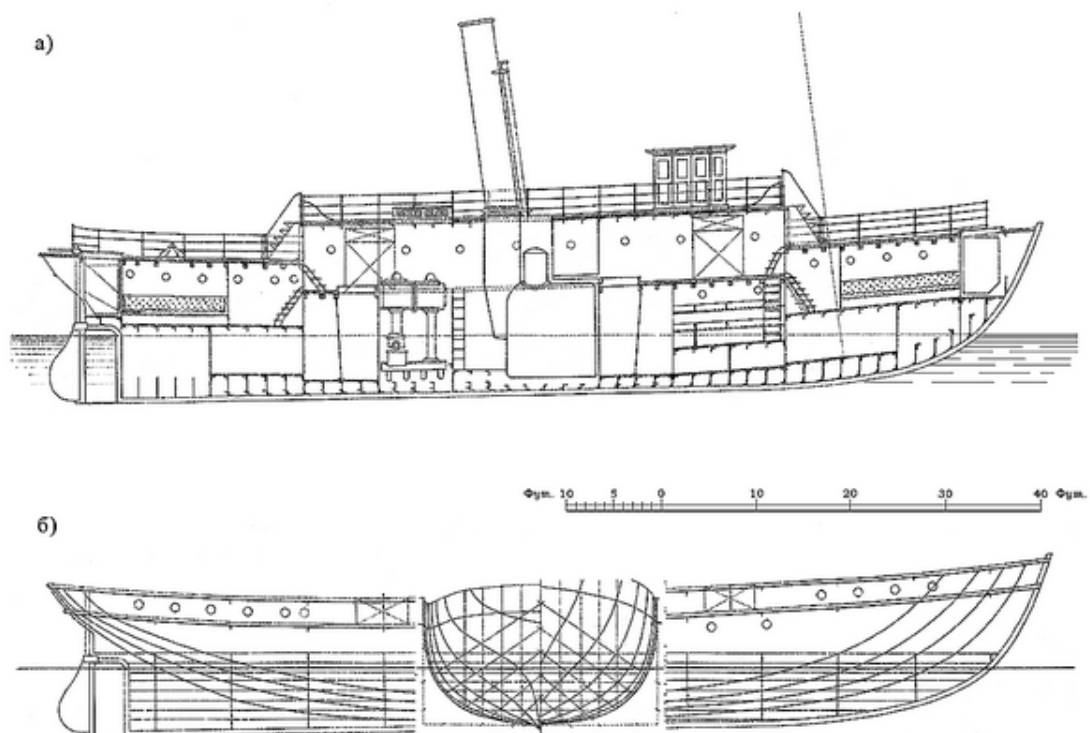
Ледокольный пароход «Оланд»: а) вид сбоку, б) теоретический чертеж
